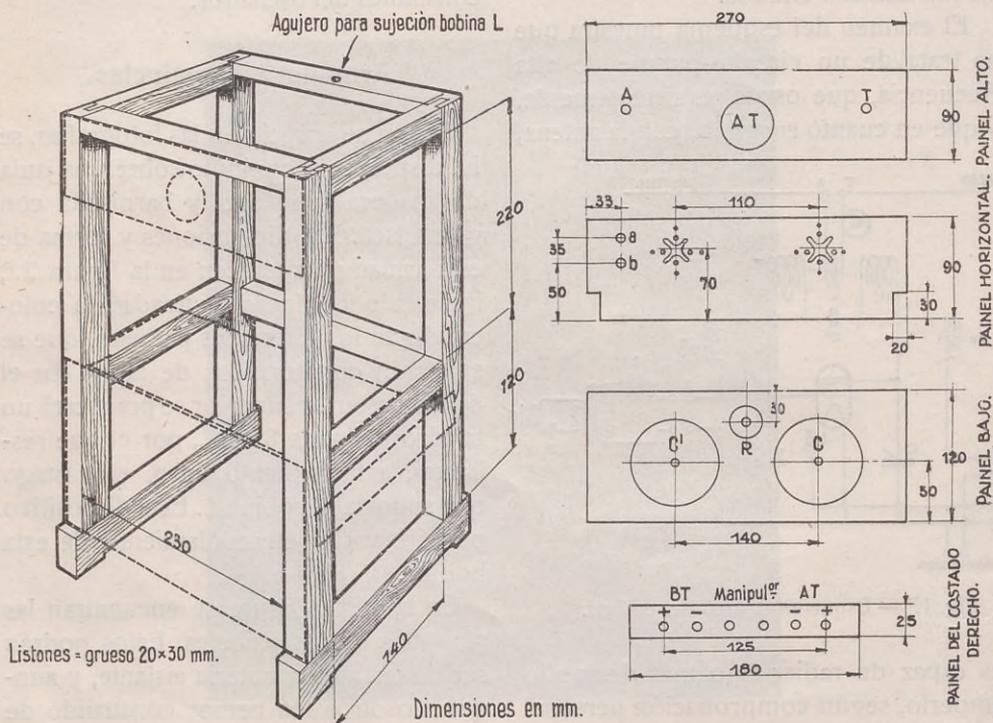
^a — Detalle de la armadura y plantilla de los paineles.
